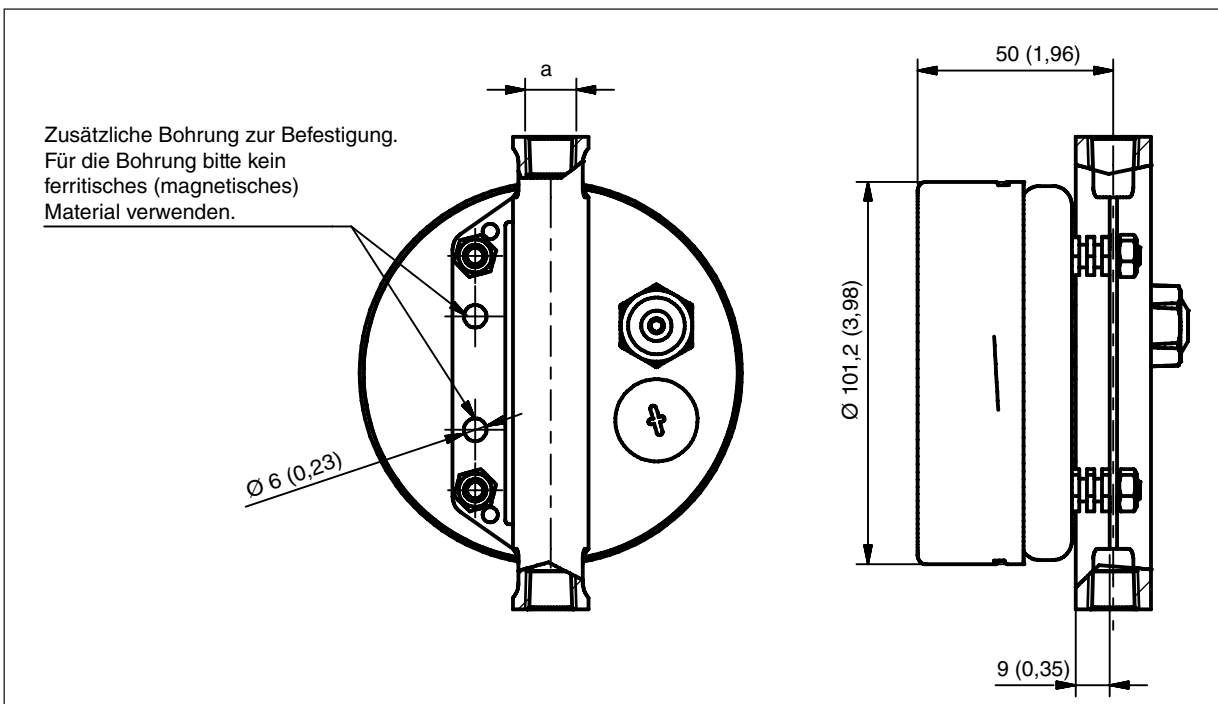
Rückansicht mit Befestigungsbohrungen, Abmessungen in mm (Zoll)
